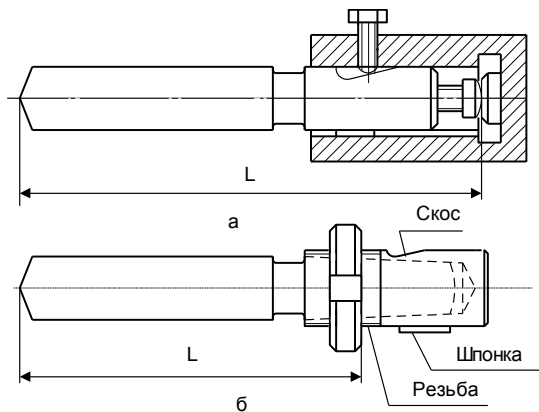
Инструменты, обеспечивающие настройку размеров вне станка
